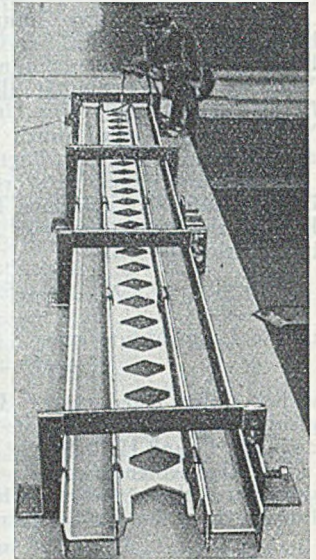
Träger mit Aussparungen auf der Schweißbank.
